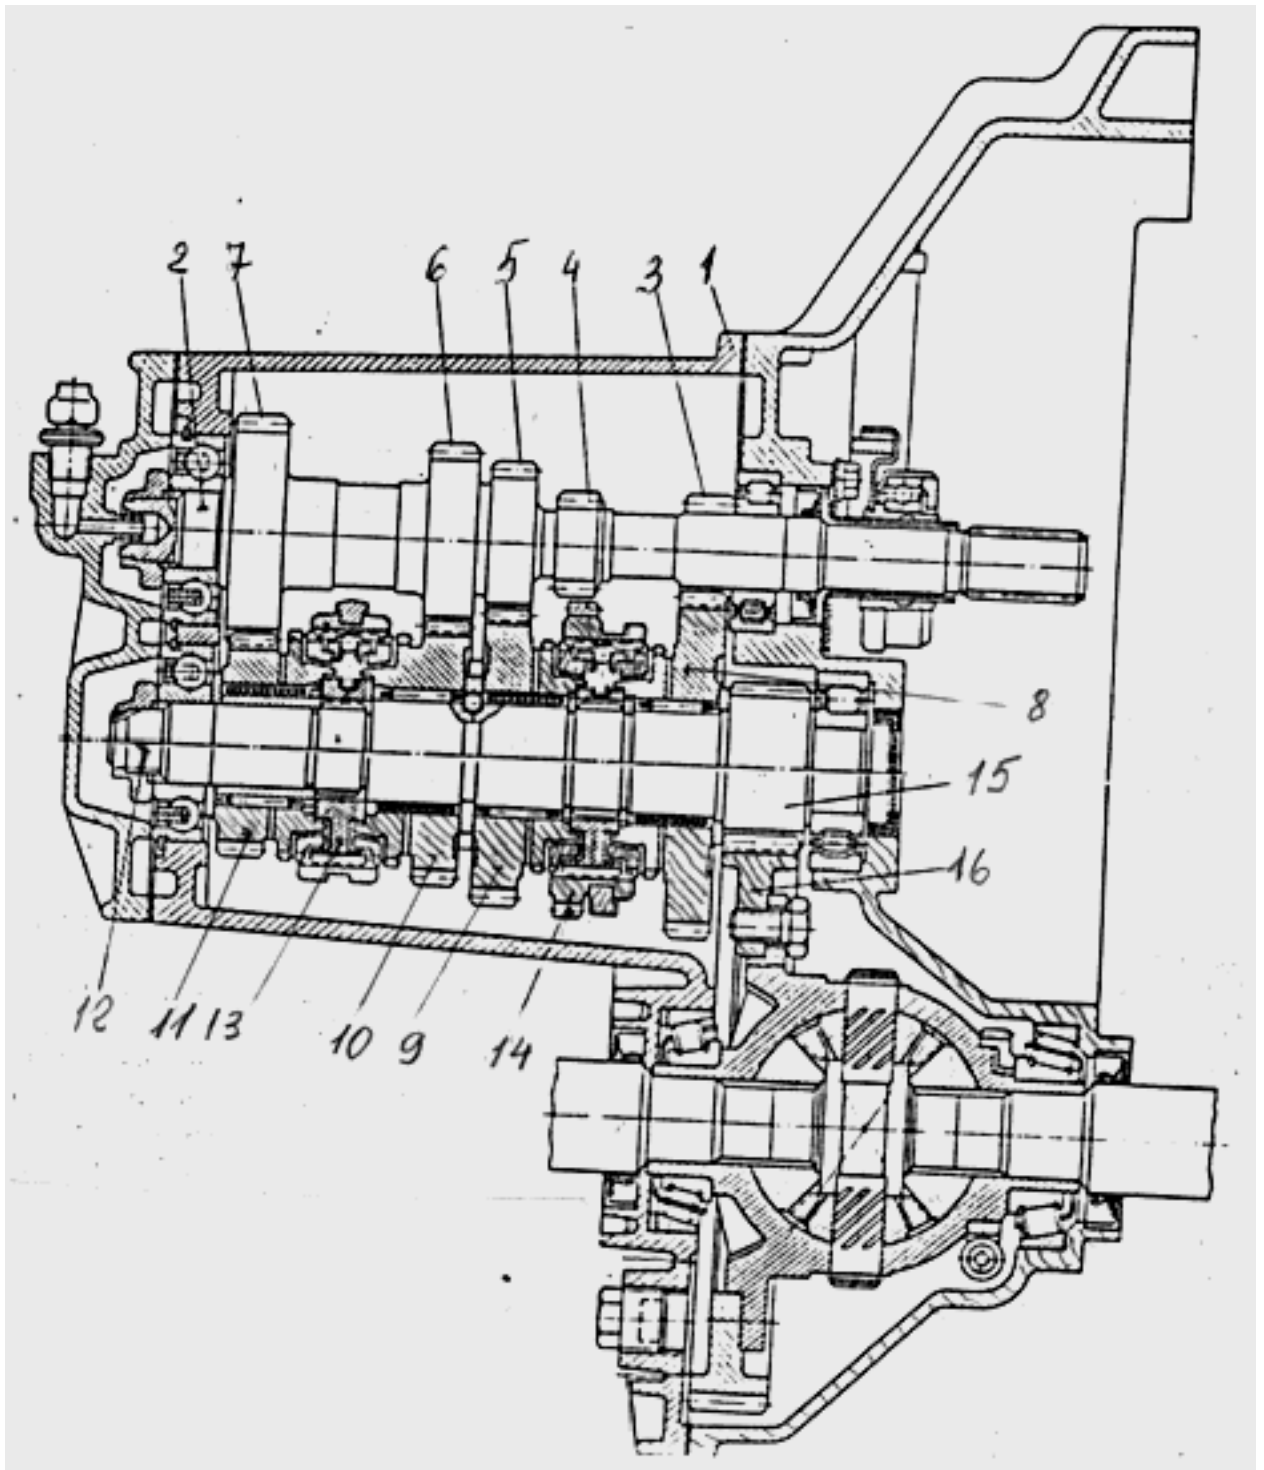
Коробка передач переднеприводного автомобиля: 1 - картер; 2 - ведущий вал; 3 - шестерня I передачи; 4 - шестерня заднего хода (ЗХ); 5 - шестерня II передачи; 6 - шестерня III передачи; 7 - шестерня IV передачи; 8 - зубчатое колесо I передачи; 9 - зубчатое колесо II передачи; 10 - зубчатое колесо III передачи; 11 - зубчатое колесо IV передачи; 12 - ведомый вал; 13 - синхронизатор III и IV передач; 14 - синхронизатор I, II передач с зубчатым колесом ЗХ; 15, 16 - шестерня и колесо постоянного зацепления
